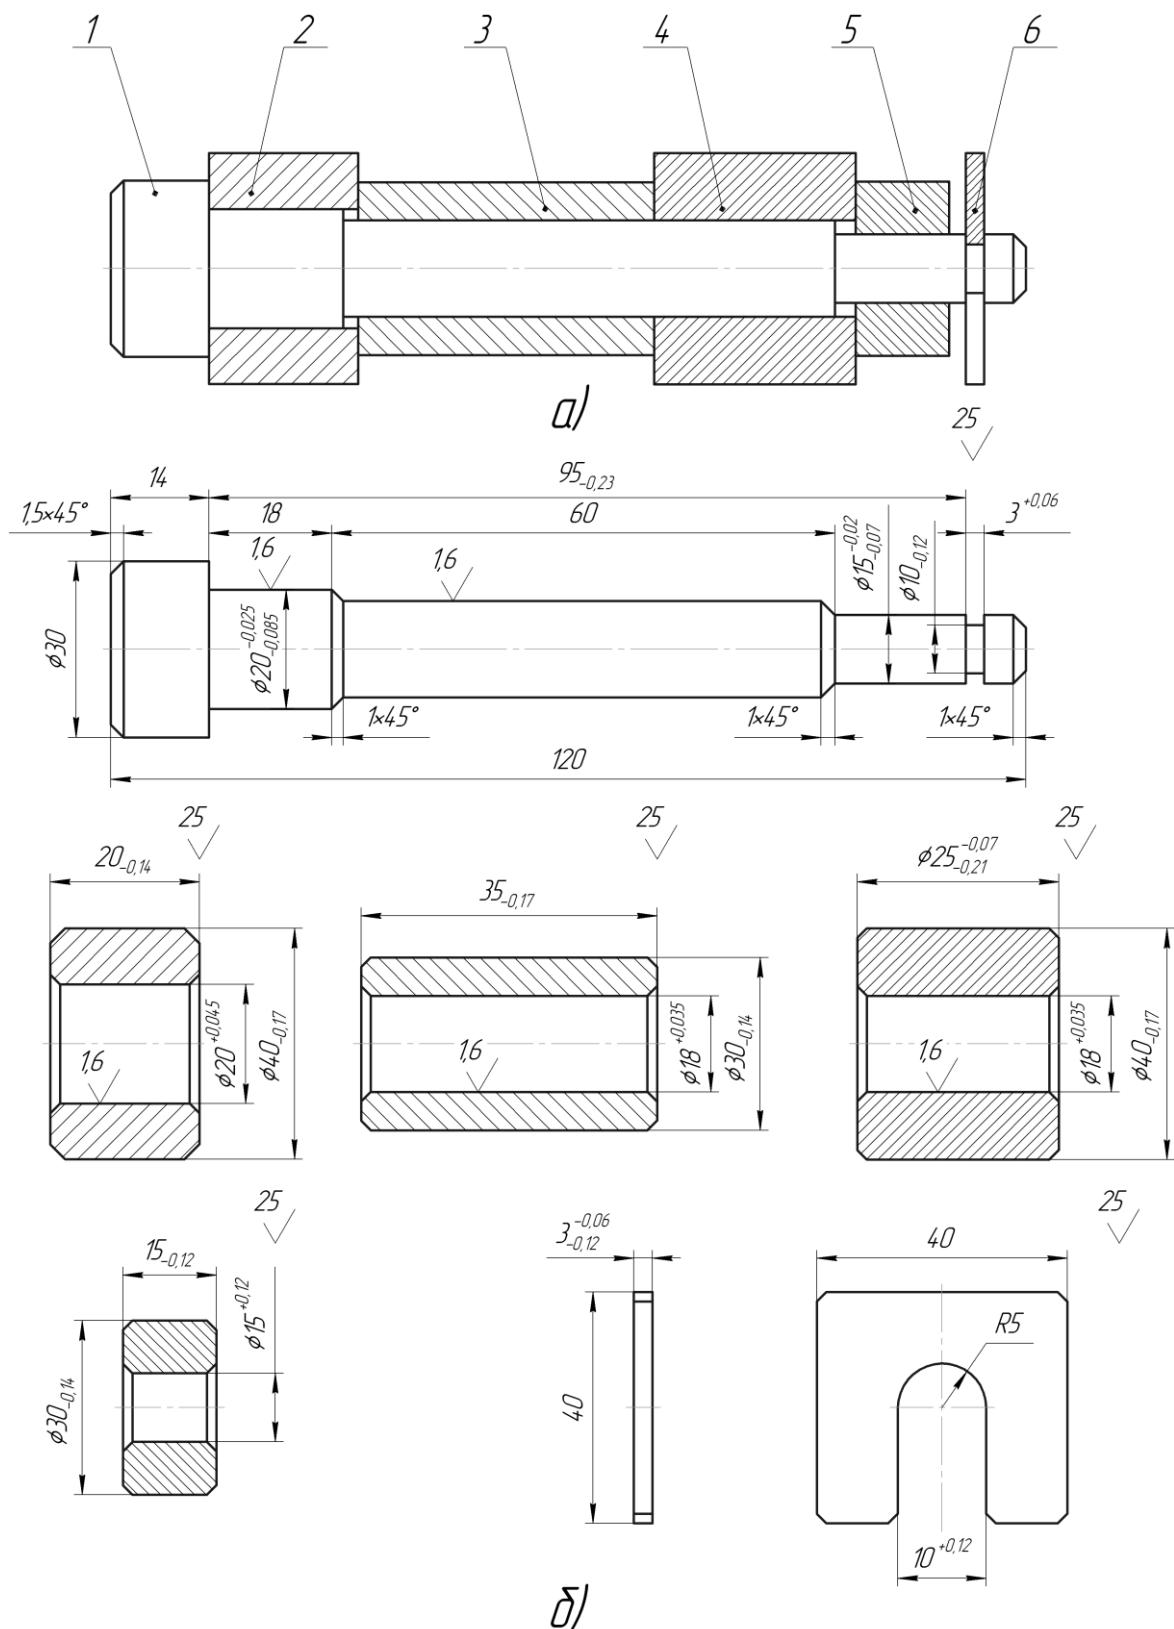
Сборочный чертеж (а) и чертежи деталей (б)
